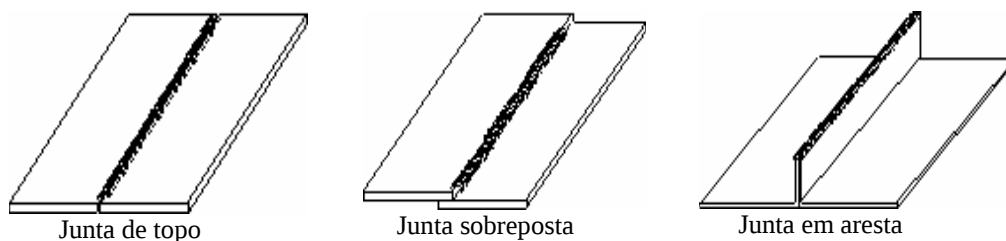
Juntas típicas para soldagem a plasma pela técnica “melt-in”
